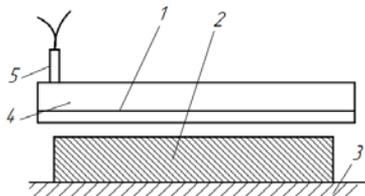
Схема плакирования сваркой взрывом плоских поверхностей:
